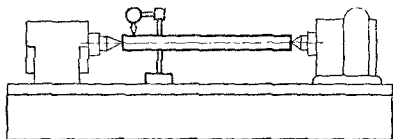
Проверка совпадения осей шпинделя и гнезда поддерживающего кронштейна горизонтально-фрезерного станка.
